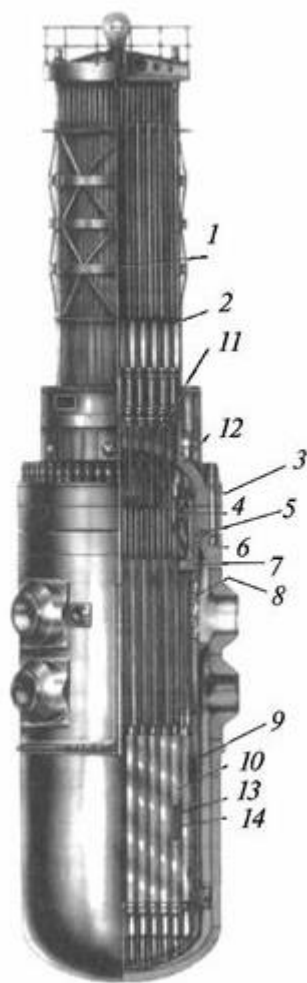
Реактор ВВЭР-1000 в сборе: 1 – верхний блок; 2 – привод СУЗ; 3 – шпилька; 4 – труба для загрузки образцов-свидетелей; 5 – уплотнение; 6 – корпус реактора; 7 – блок защитных труб; 8 – шахта; 9 – выгородка активной зоны; 10 – топливные сборки; 11 – теплоизоляция реактора; 12 – крышка реактора; 13 – регулирующие стержни; 14 – топливные стержни
